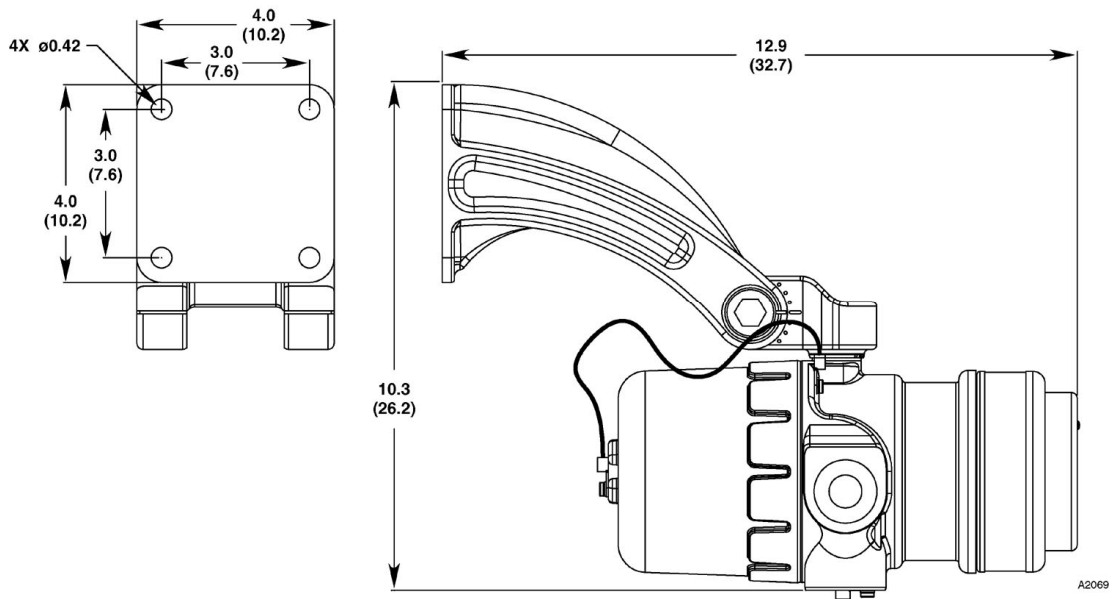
Габаритные и установочные размеры извещателя с монтажным кронштейном Q9033B в дюймах (см).
